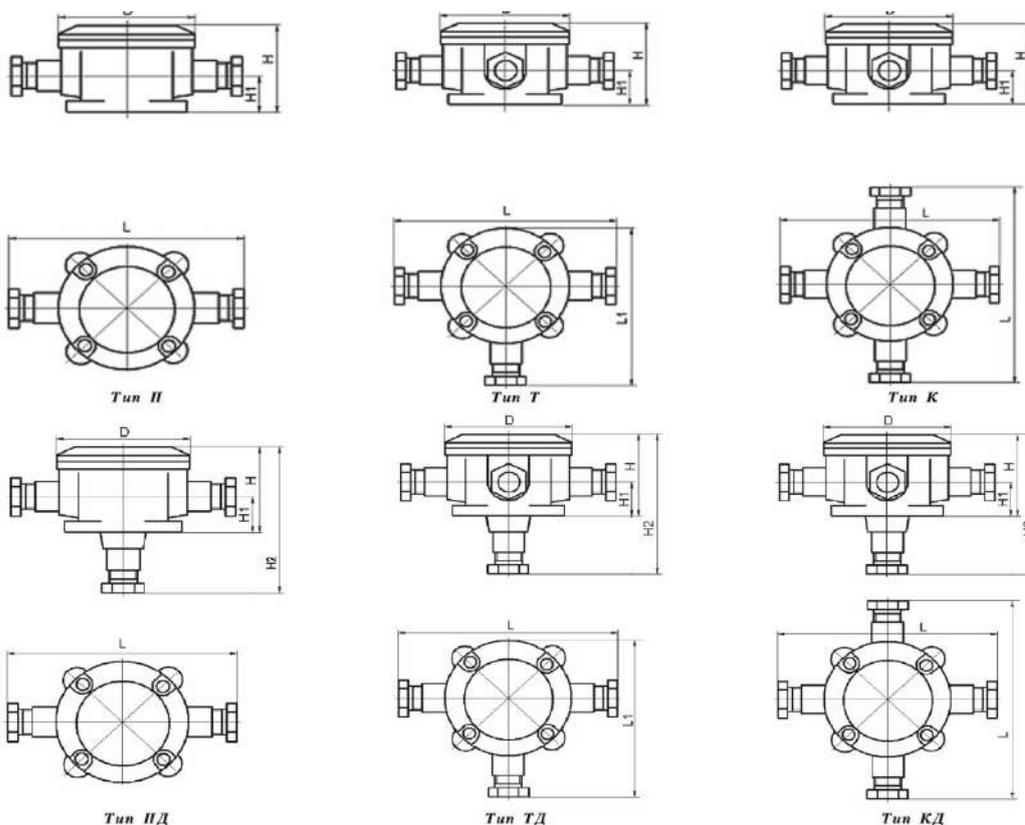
Общий вид коробок ExКСУВ-А-ПД из алюминиевого сплава.
